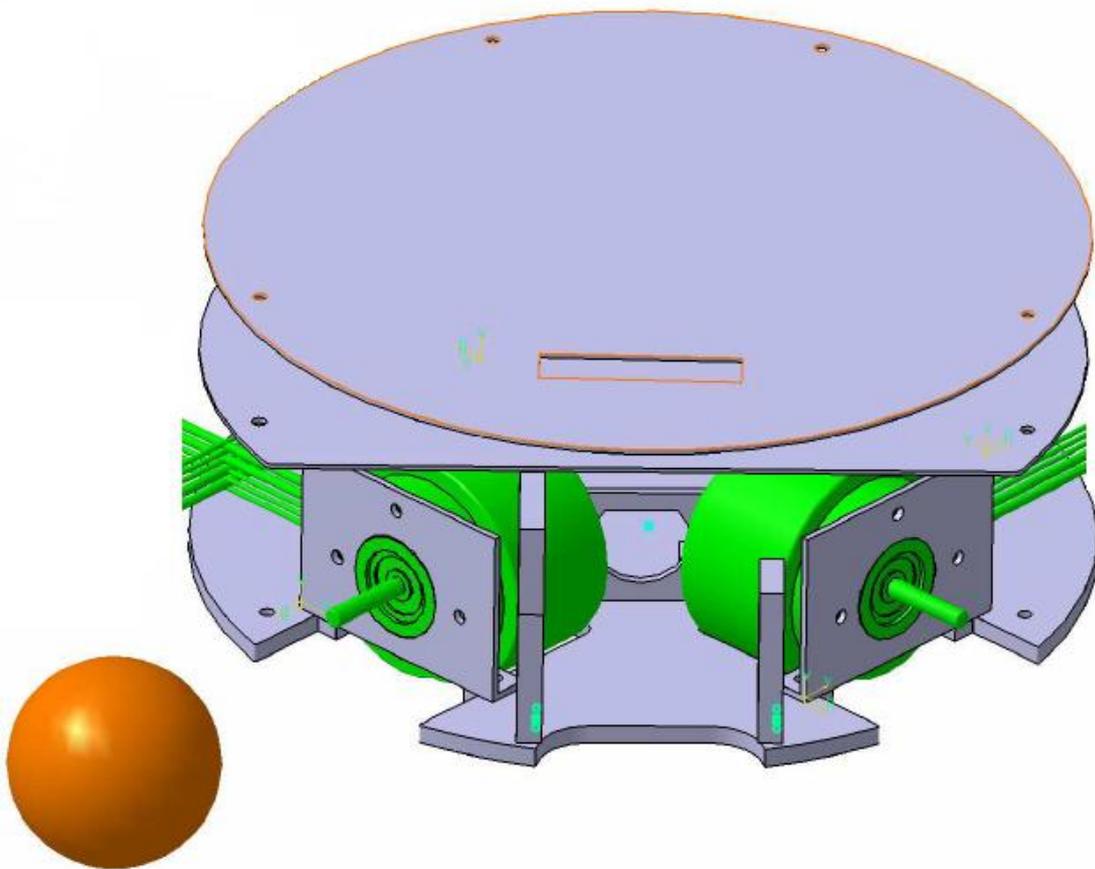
49 Ubicación de la Base segunda planta en el conjunto Robot
